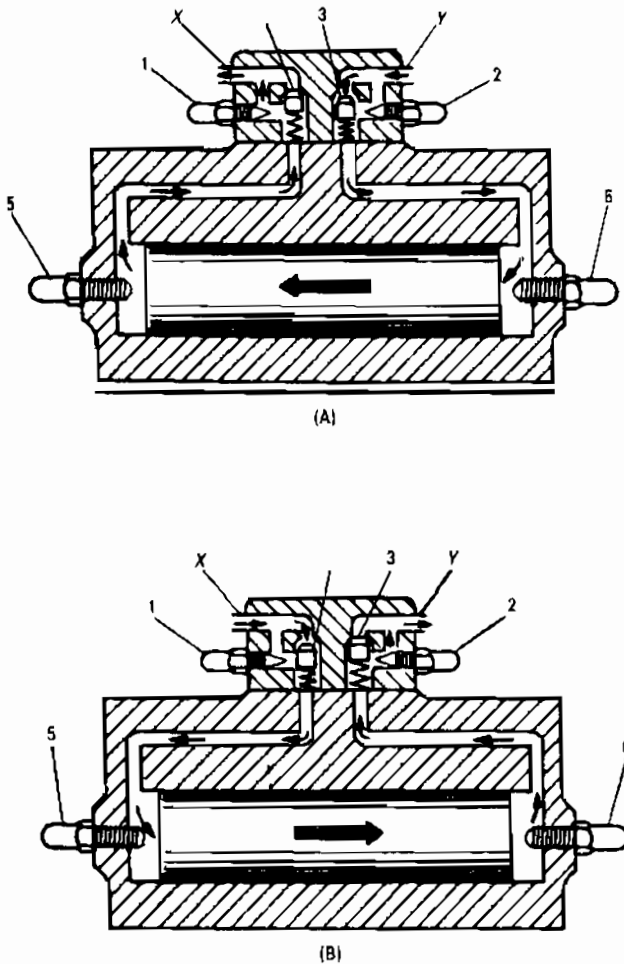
Valve điều khiển hướng vận hành bằng trục cam.
